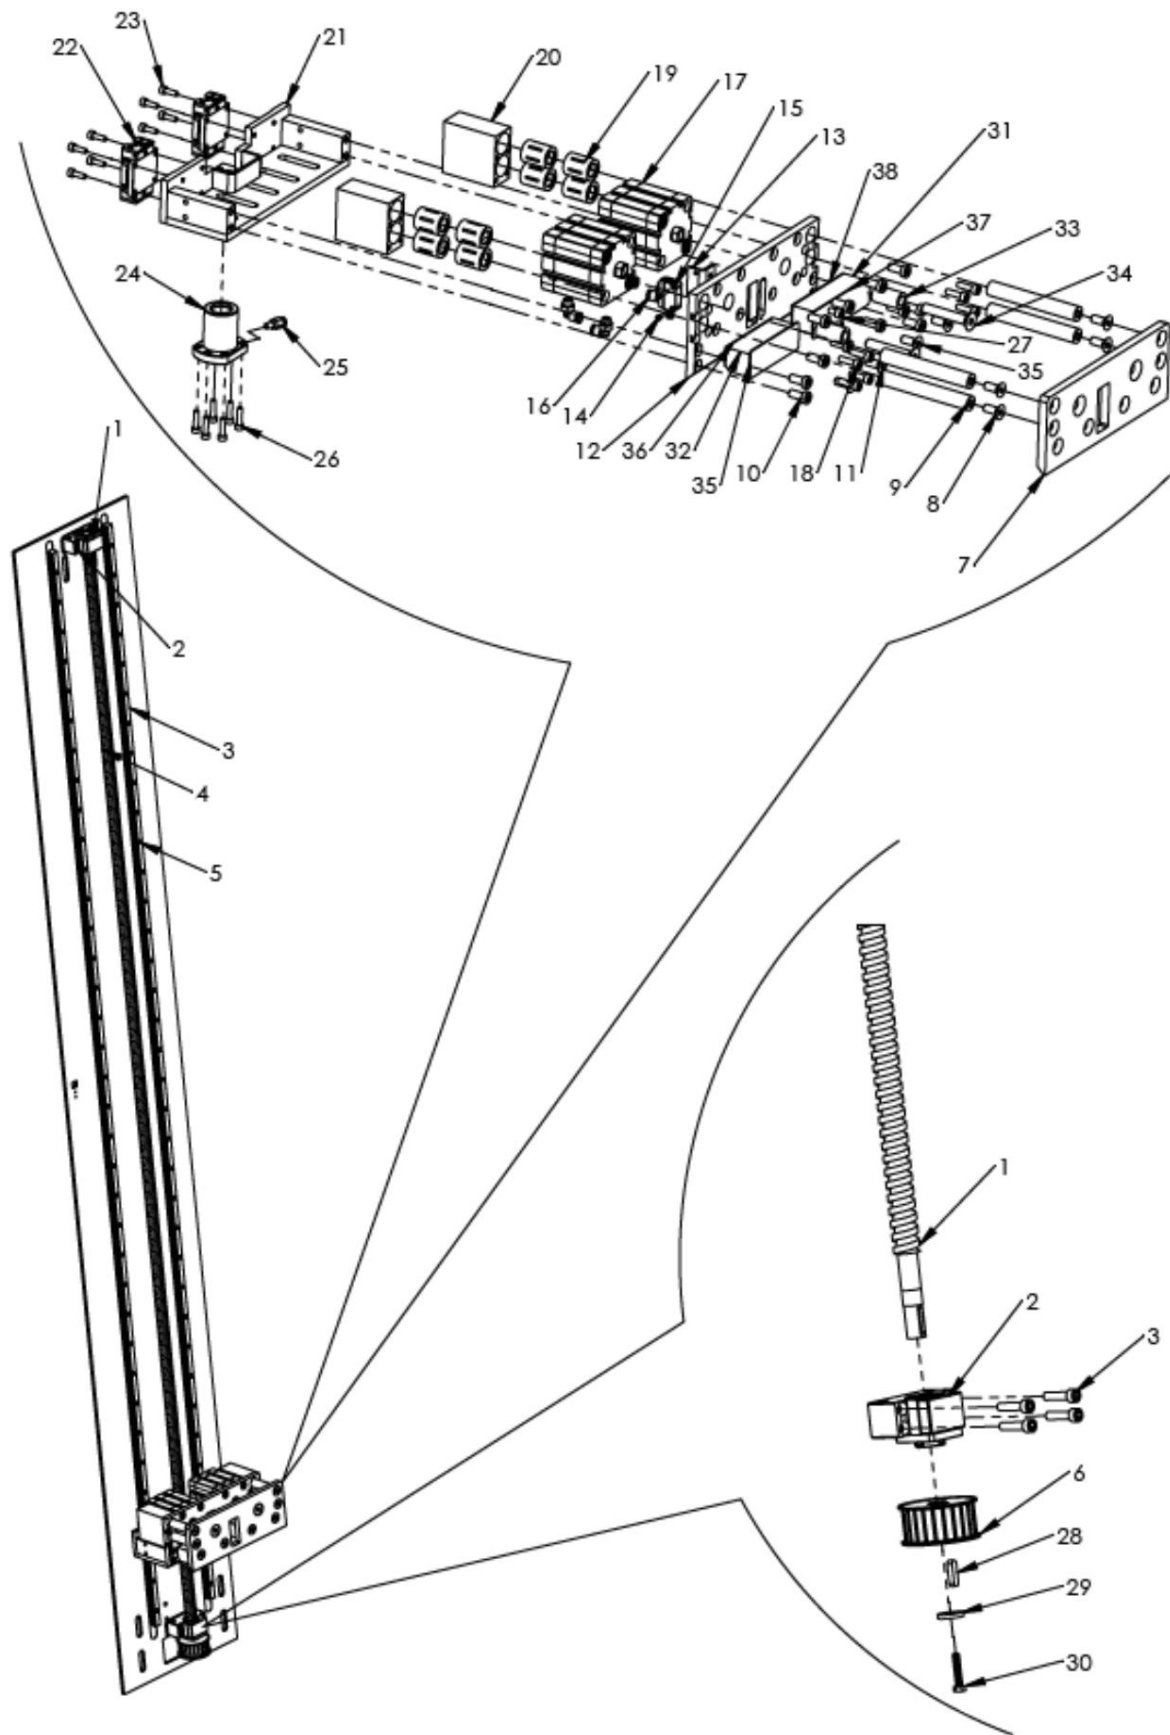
Dibujo de piezas de repuesto 24 - VPS 22-51 VR ED KS
